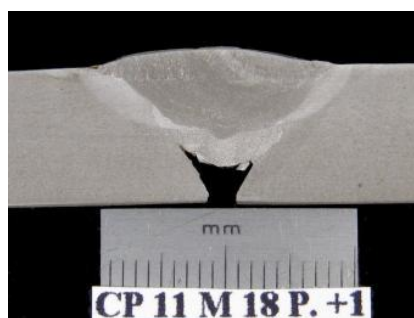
Defeitos na soldadura, adaptado de [44].
